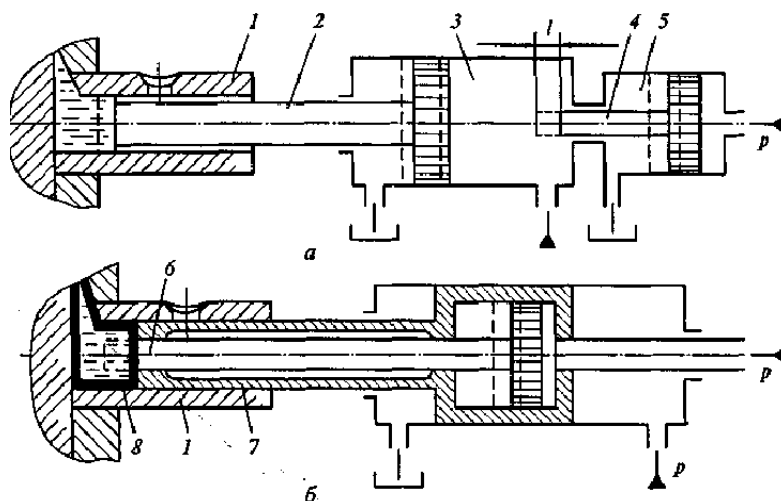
Схемы механизмов прессования машин литья под давлением: а – с мультипликатором; б - с двойным плунжером; 1 - камера прессования; 2 - шток основного гидроцилиндра с пресс-поршнем; 3 - основной гидроцилиндр; 4 - шток мультипликатора; 5 - мультипликатор; 6 - дополнительный плунжер; 7 - основной плунжер; 8 - затвердевший металл.
